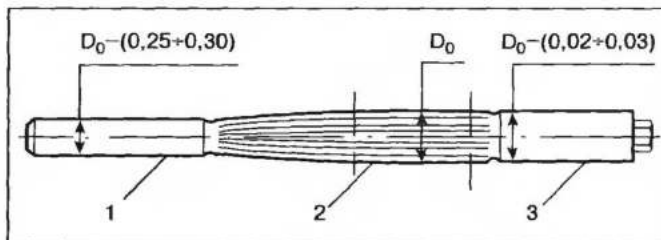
Специальная развертка для ремонта отверстий подшипников распределительного вала:
